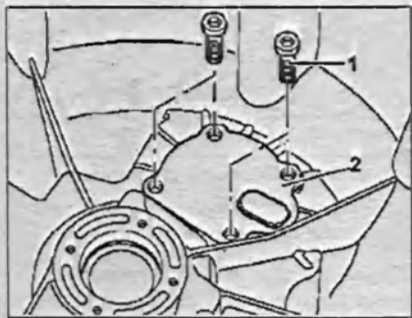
Снимите крышку подшипника 2, открутив болты 1.
